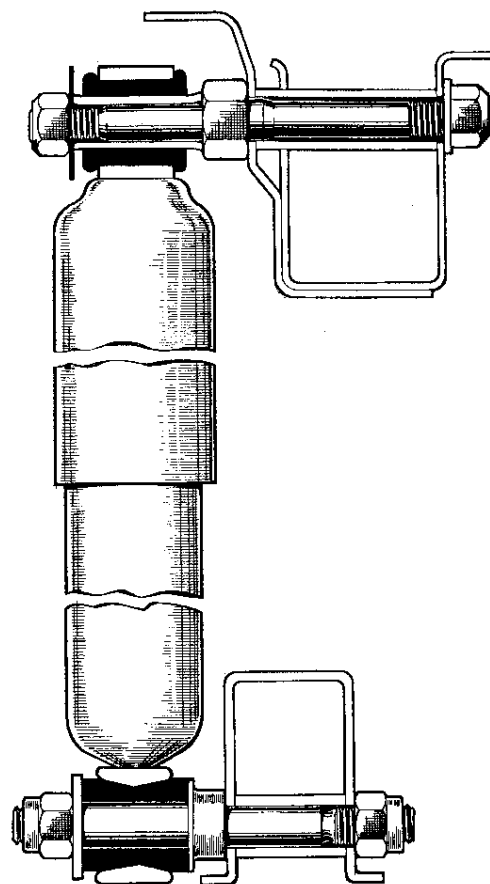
Hintere Stoßdämpferbefestigung (spät. Ausf.)
